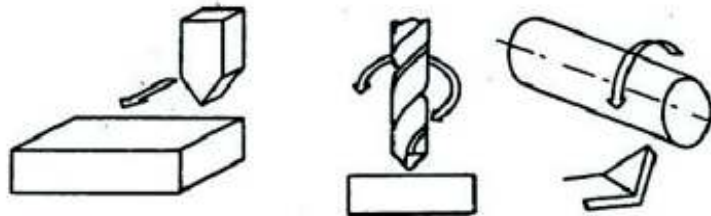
Movimiento principal de corte transmitido por máquina-herramienta.
